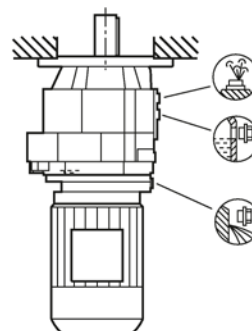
Монтажные положения для цилиндрического редуктора DF/ZF в исполнении с фланцем и DZ/ZZ с фланцем корпуса, типоразмер 39
